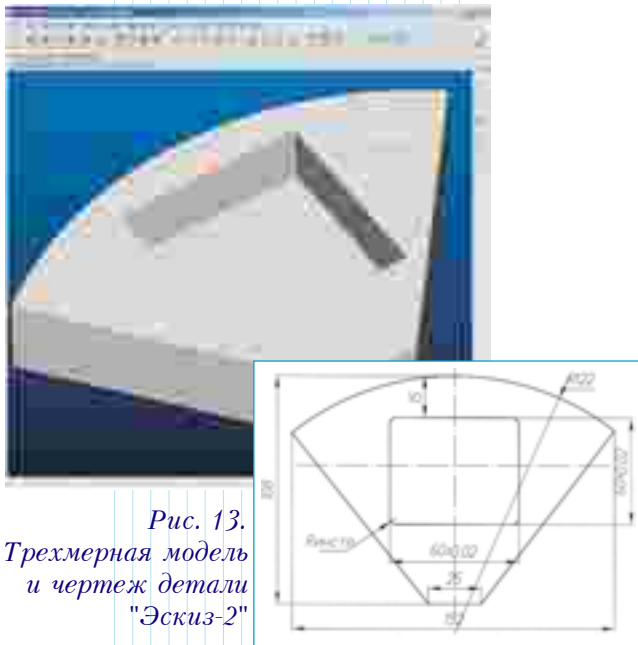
Трехмерная модель и чертеж детали “Эскиз-2”
